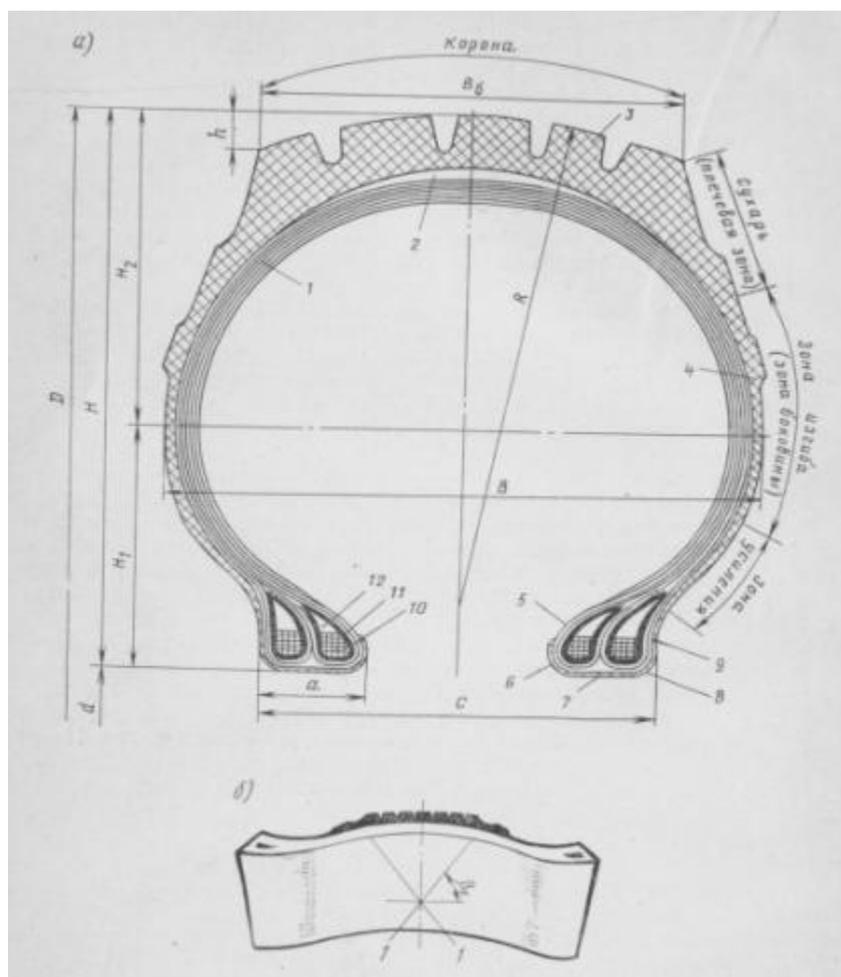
Радиальный срез шины: а) основные конструктивные элементы и размеры покрышки: 1-каркас; 2-подушечный слой (брокер); 3-протектор; 4-боковина; 5-борт; 6-носик борта; 7-основание борта; 8-пятка борта; 9-бортовая лента; 10-бортовая проволока; 11-обертка; 12-наполнительный шнур; H-высота профиля покрышки; H₁-расстояние от основания борта до горизонтальной осевой линии профиля; H₂-расстояние от горизонтальной оси до экватора; B-ширина профиля покрышки; B_б-ширина беговой дорожки протектора по хорде (корона); R-радиус кривизны протектора; D-наружный диаметр шины; d-внутренний (посадочный) диаметр шины; h-стрела дуги протектора; C-ширина раствора бортов; a-ширина борта; б-угол β_k нити корда по короне; 1-нити корда
